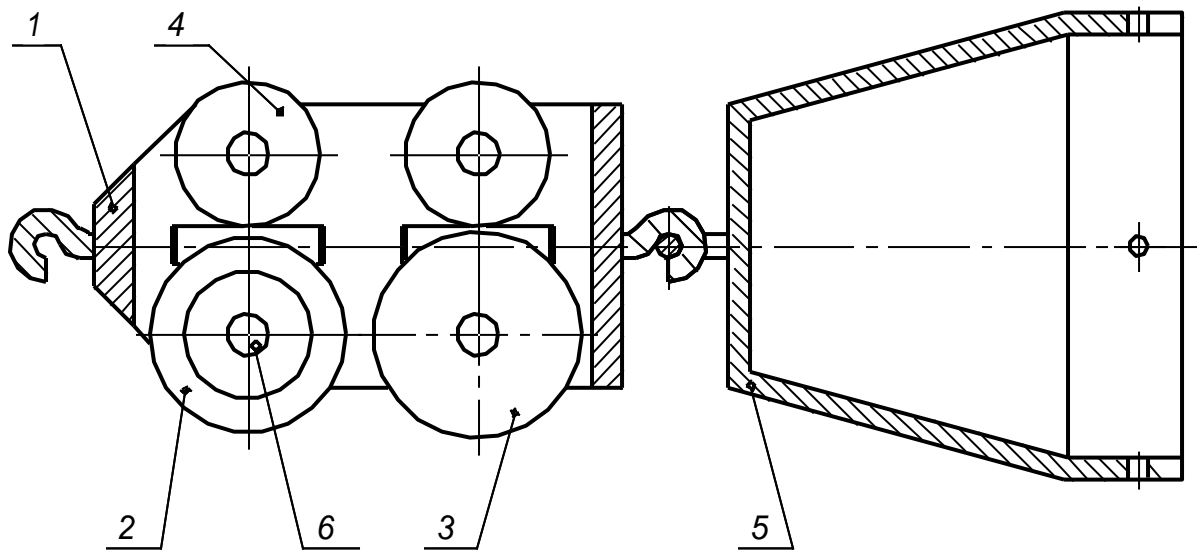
Предлагаемый образец натурального рабочего органа (продольное сечение): 1 – корпус рабочего органа; 2 – дисковый нож для надрезания старого трубопровода; 3 – ролик для дорыва предварительно надрезанного старого трубопровода; 4 – опорные катки; 5 – расширитель; 6 – оси
